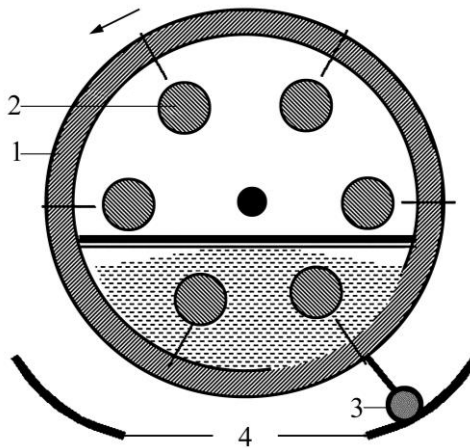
Установка для ПЭХТО во вращающейся ванне: 1 – барабан; 2 – обрабатываемая деталь; 3 – ползун; 4 – неподвижная колодка [129].
